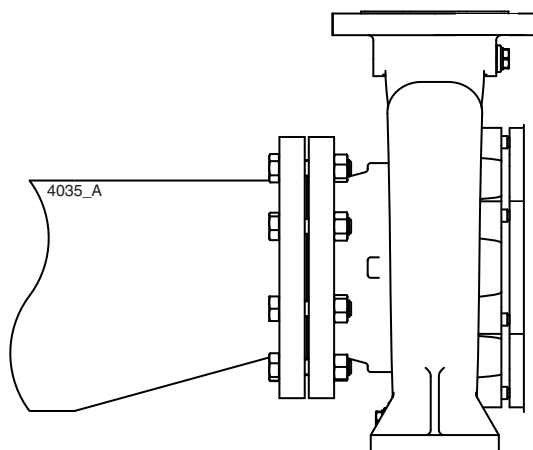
Переходной патрубок с эксцентричным расположением концевых отверстий для приемного фланца.
